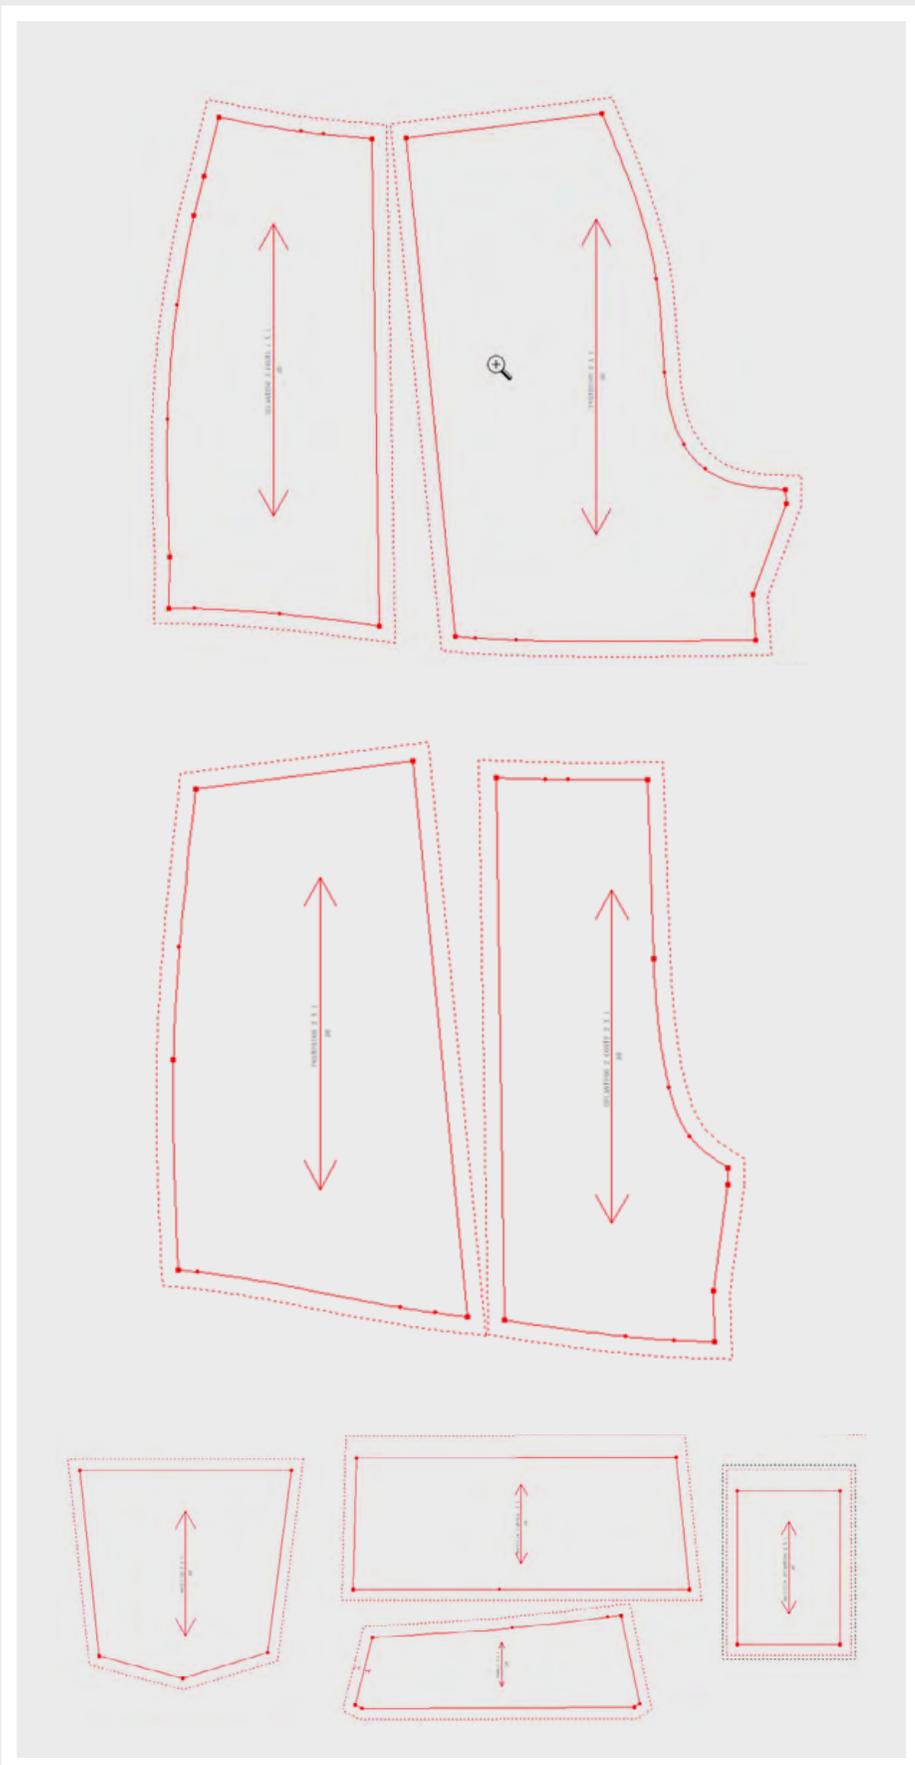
Patrones short outfit 1. Fuente (Autoría propia, 2020)
